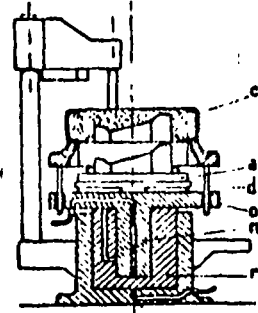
La misma máquina de la figura precedente. El plato está desviado lateralmente y la máquina en la fase de desmoldar.
